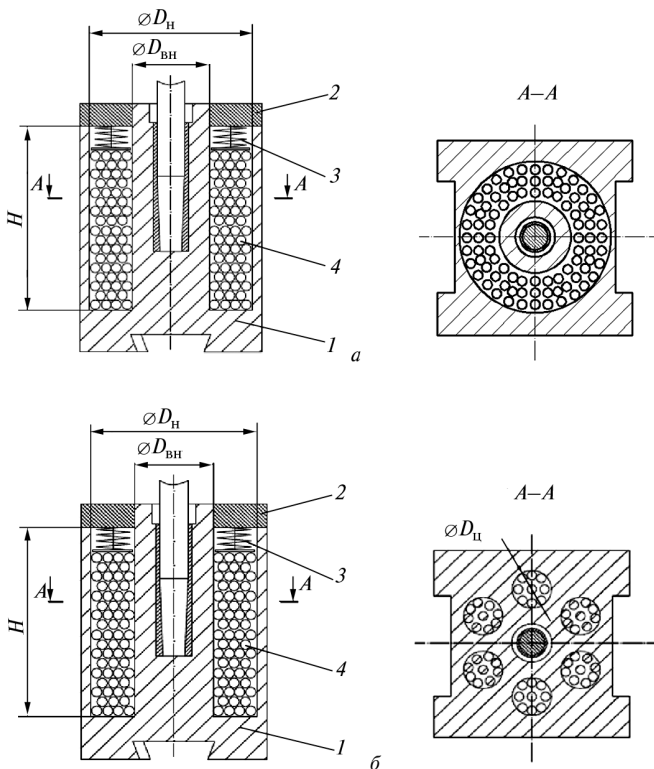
Схема бабы ковочного молота с наполнителем с внутренней кольцевой полостью (а) и с внутренней полостью в виде  $N$  отверстий (б): 1 — корпус бабы; 2 — крышка бабы; 3 — пружина; 4 — наполнитель (шарики)
